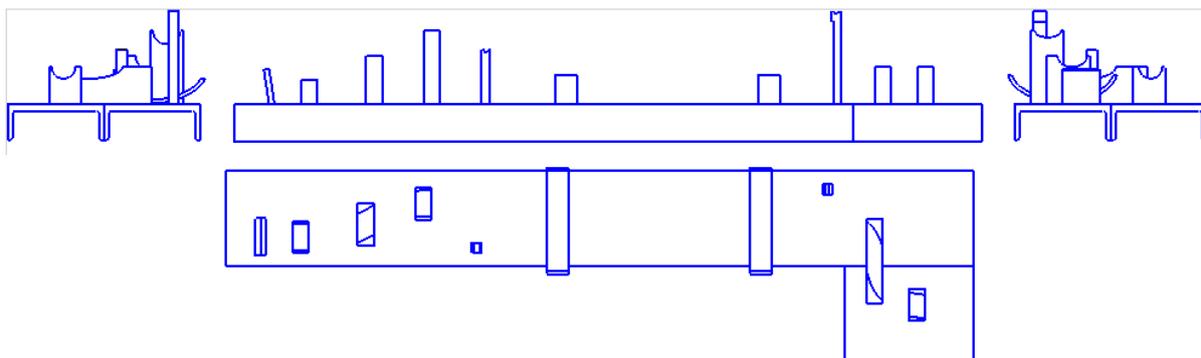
Эскиз сборочного кондуктора без глушителя
